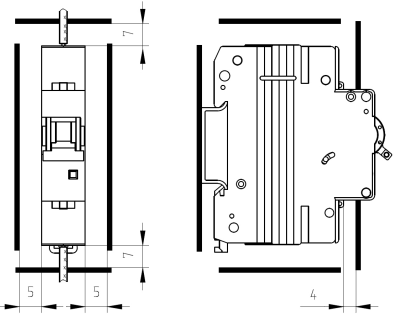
Форма и размеры проводника, подготовленного для присоединения к выключателю
